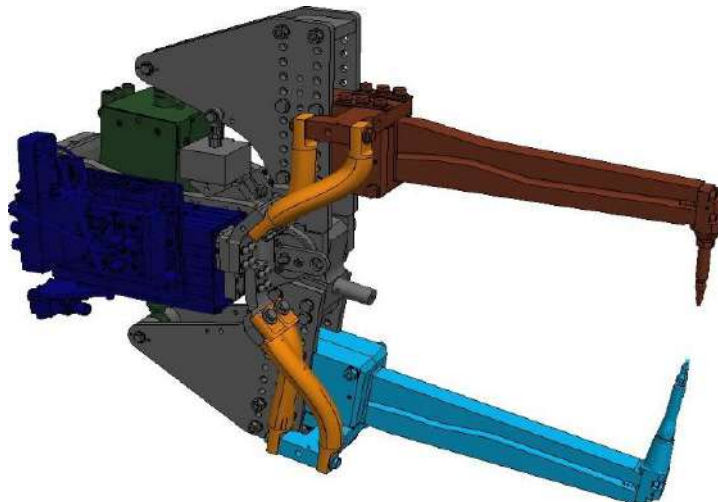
Зварювальний пістолет для пристрою 0R03 тип X
